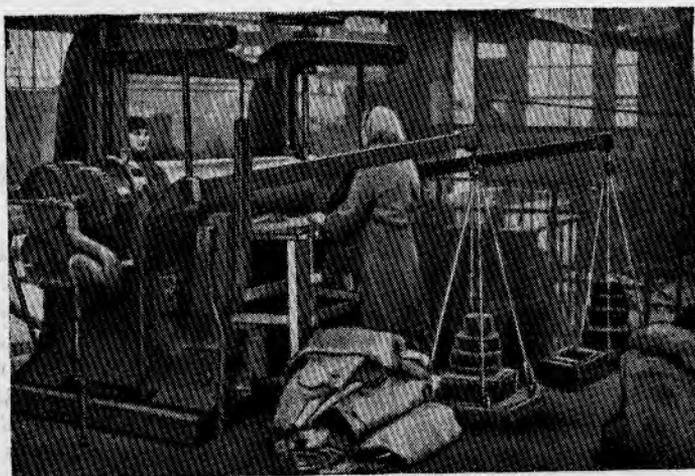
Однопарный валцовый пресс—реконструированный гладильный каландр, установленный на кожевном заводе им. Л. М. Кагановича.
